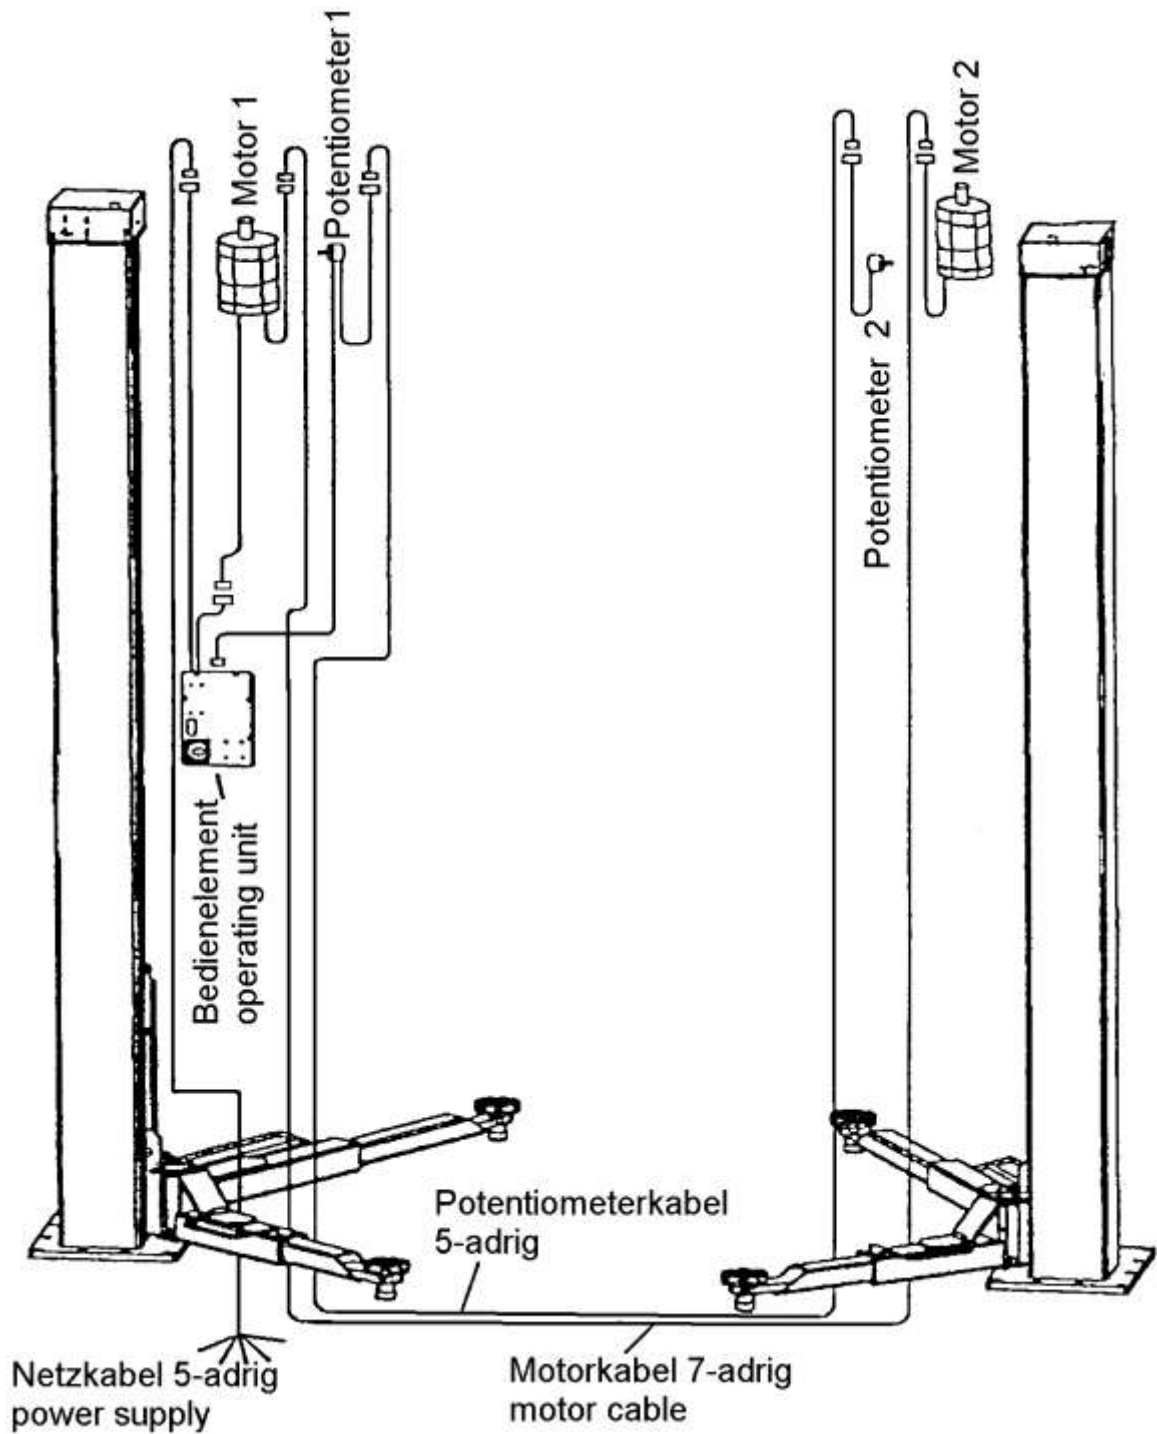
Recorrido de los cables sin el uso de tubo vertical y transversal
